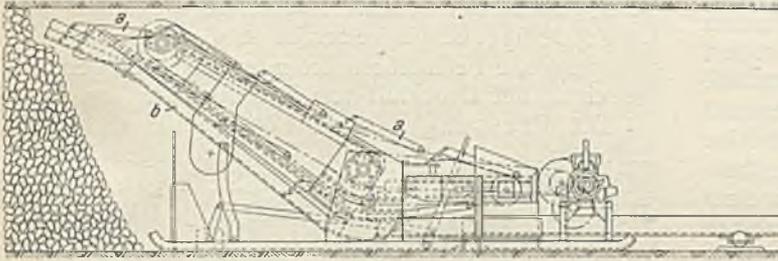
Längsschnitt durch die Versatzmaschine der Carlshütte.
